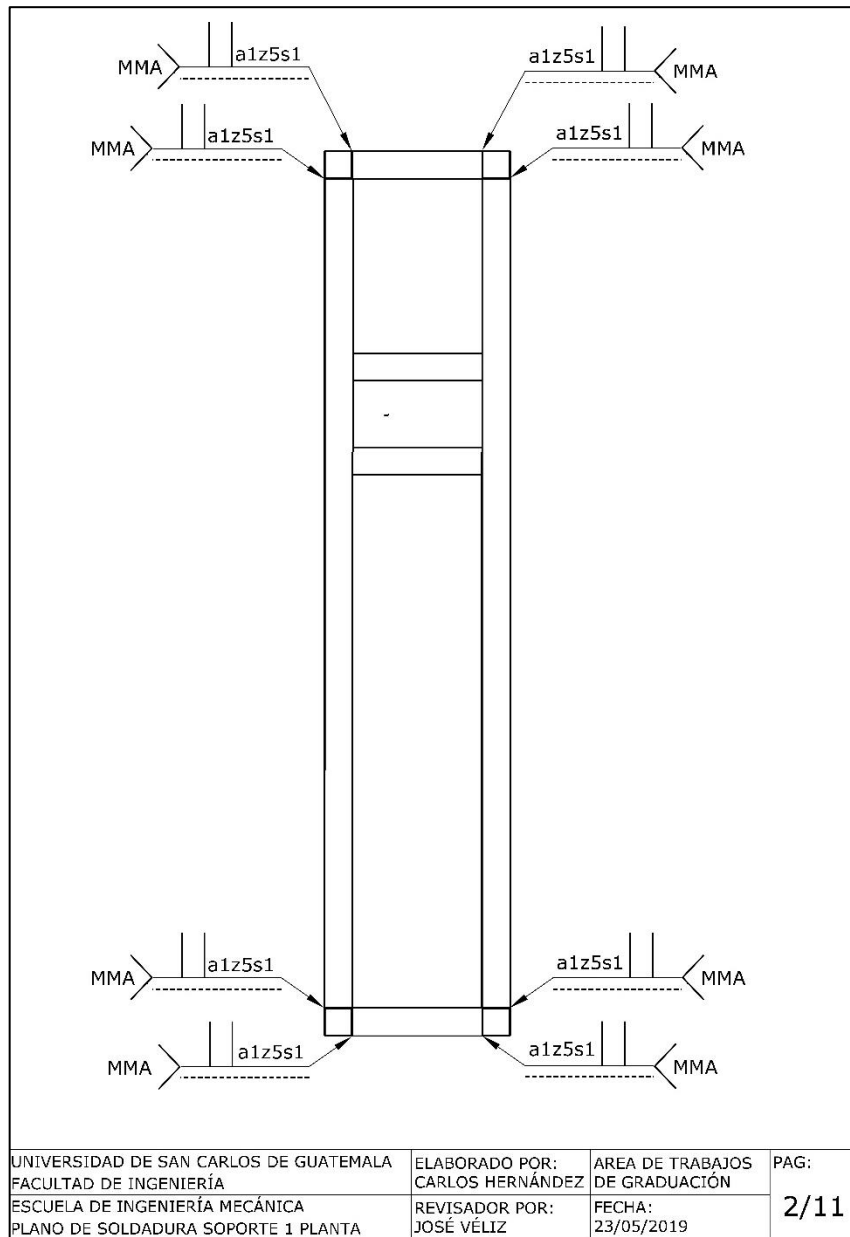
Plano de soldadura del soporte de tubería vista frontal
